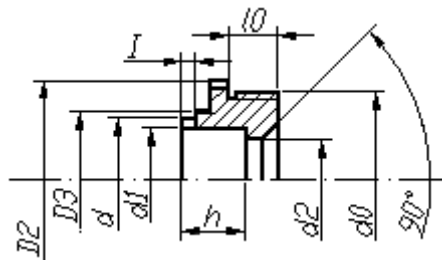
Оправа для завальцовки. Закатка с внешней стороны.
